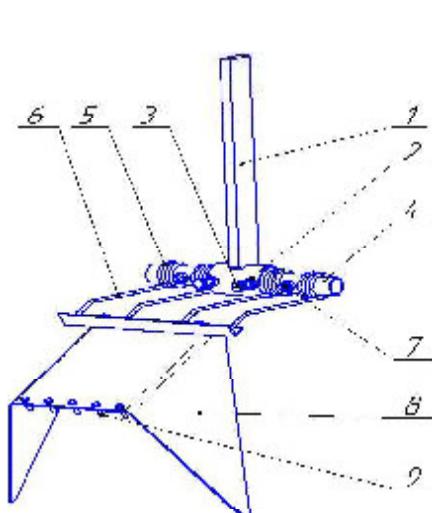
Схема профилеформователя узкопрофильных гряд для установки на агрегат универсальный АУ-М2 (вид с боку)
